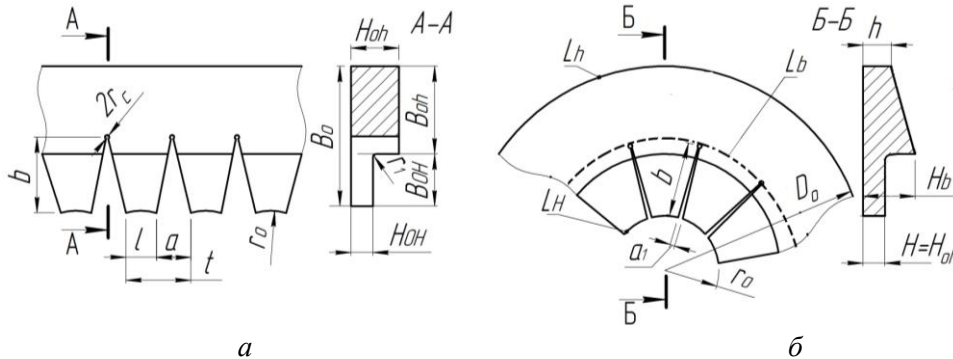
Розрахункова схема для визначення конструктивних параметрів ШГЗ:
